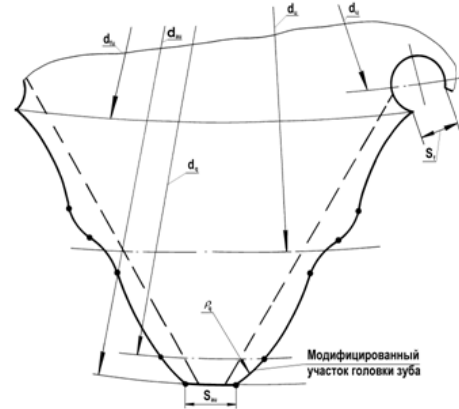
Профиль зуба шевера для обработки колес передач Новикова
